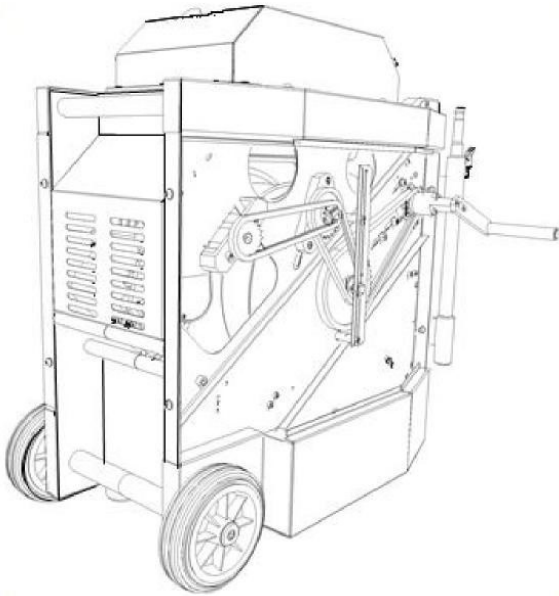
Handkurbel für die motorisierte Kabeltrommel.
